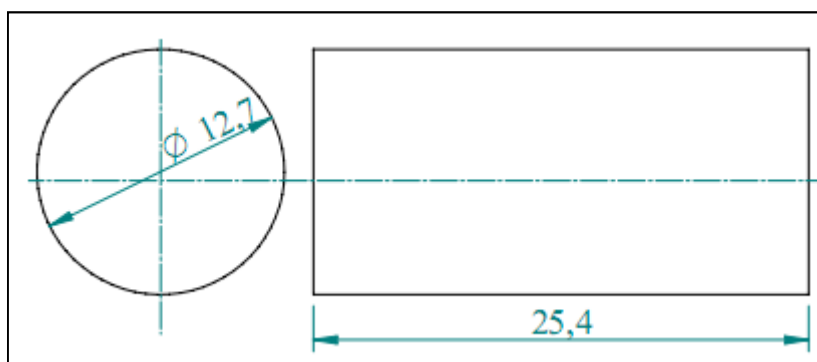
Dimensões do corpo de prova de compressão [mm]
